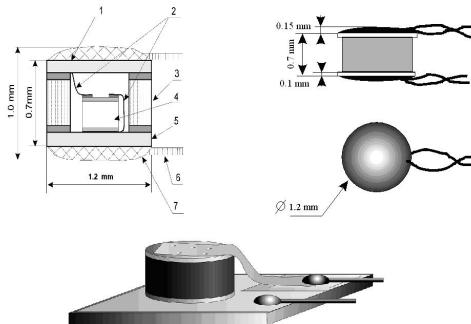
Загальний вигляд і конструкція корпусу термометра: 1, 5 – мідні позолочені кришки корпусу; 2 – контактні виводи; 3 – металокерамічна втулка; 4 – термочутливий елемент; 6 – зовнішні контактні виводи; 7 – олов'яній припій.
